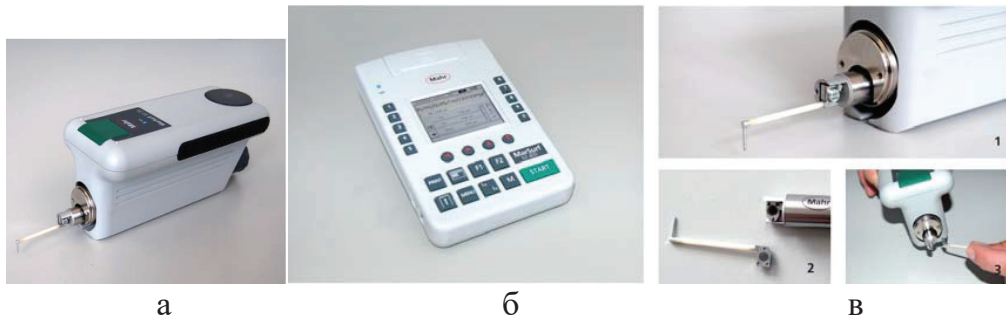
Прибор для измерений шероховатости поверхности MarSurf M 400: а – блок привода SD26; б – прибор MarSurf M 400; в – рычаг датчика с магнитным держателем
